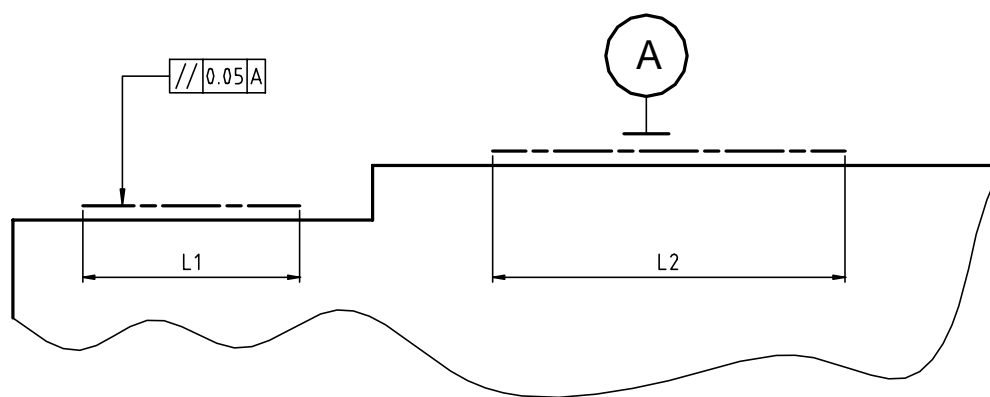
6 限定形位公差的被测要素和基准要素的范围
